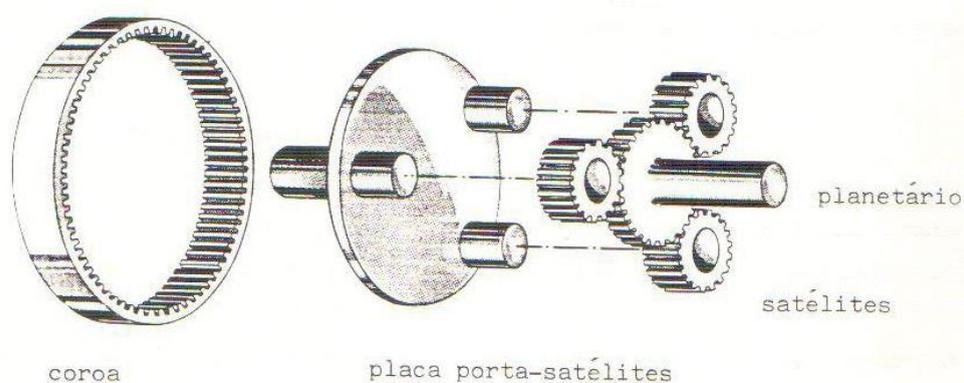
Vista explodida de arranjo especial de engrenagens cilíndricas de dentes retos conhecido como conjunto planetário.
